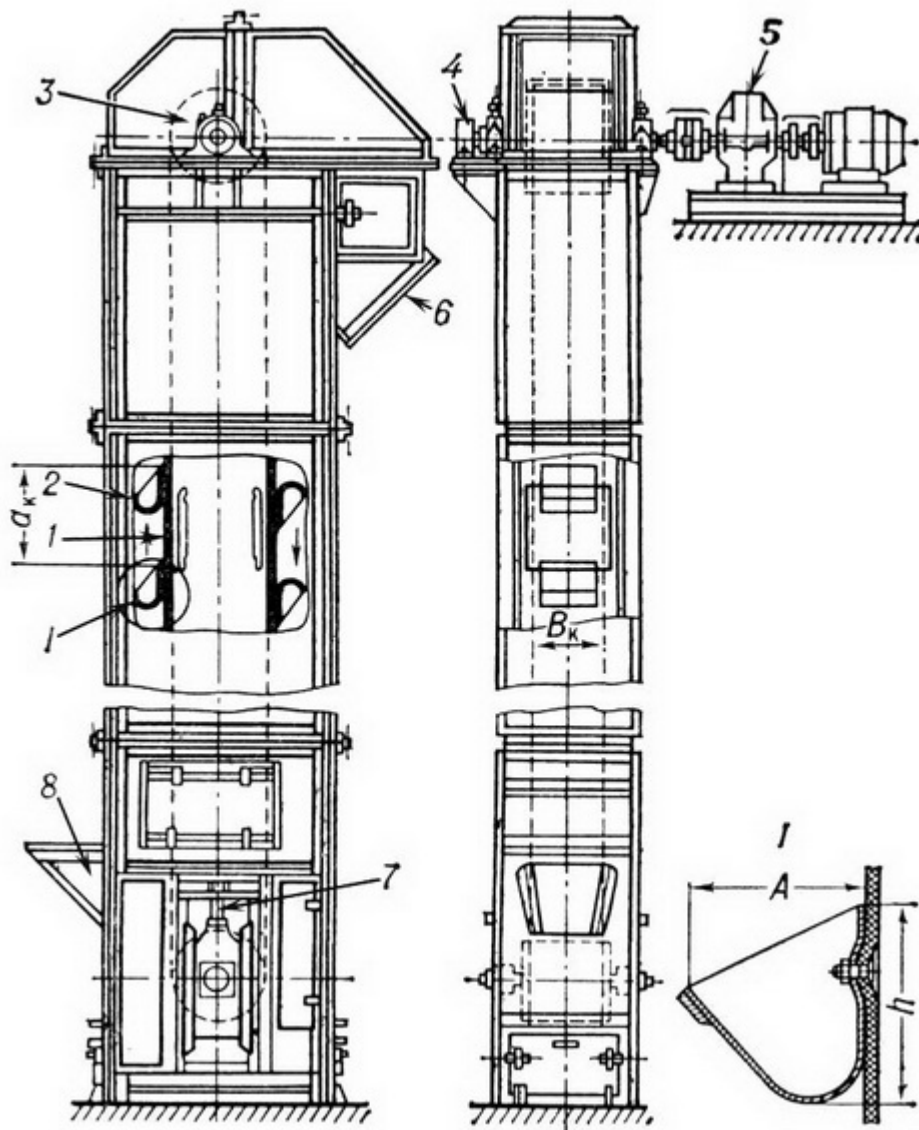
Вертикальный ковшовый ленточный элеватор
